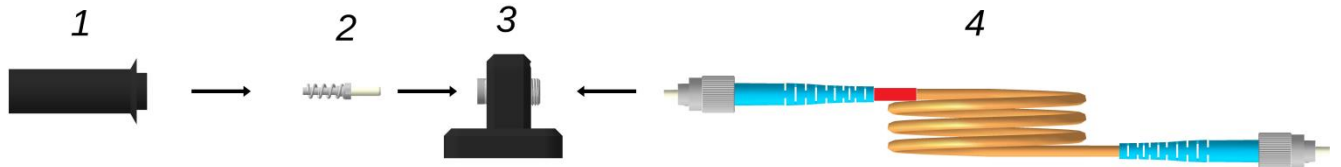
Состав АГВ. 1 - ловитель, 2 - ферула , 3 – корпус с оптической розеткой, 4 – оптический патчкорд ШОС-И.
